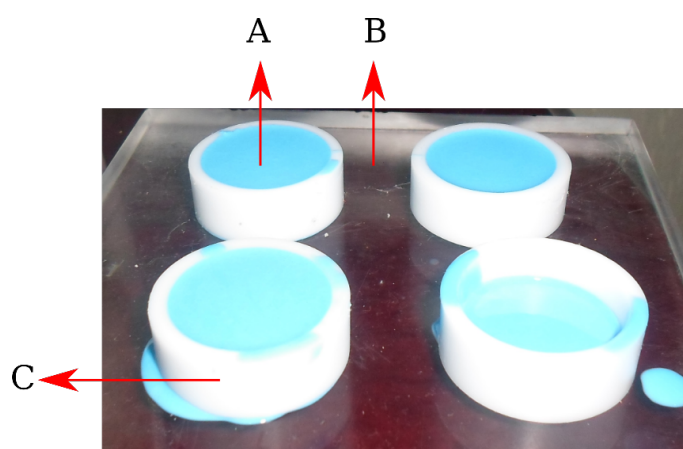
Moldagem dos elastômeros – Moldagem do Elastômero Azul. Sendo A o elastômero, B uma placa de acrílico e C o dispositivo de moldagem.
